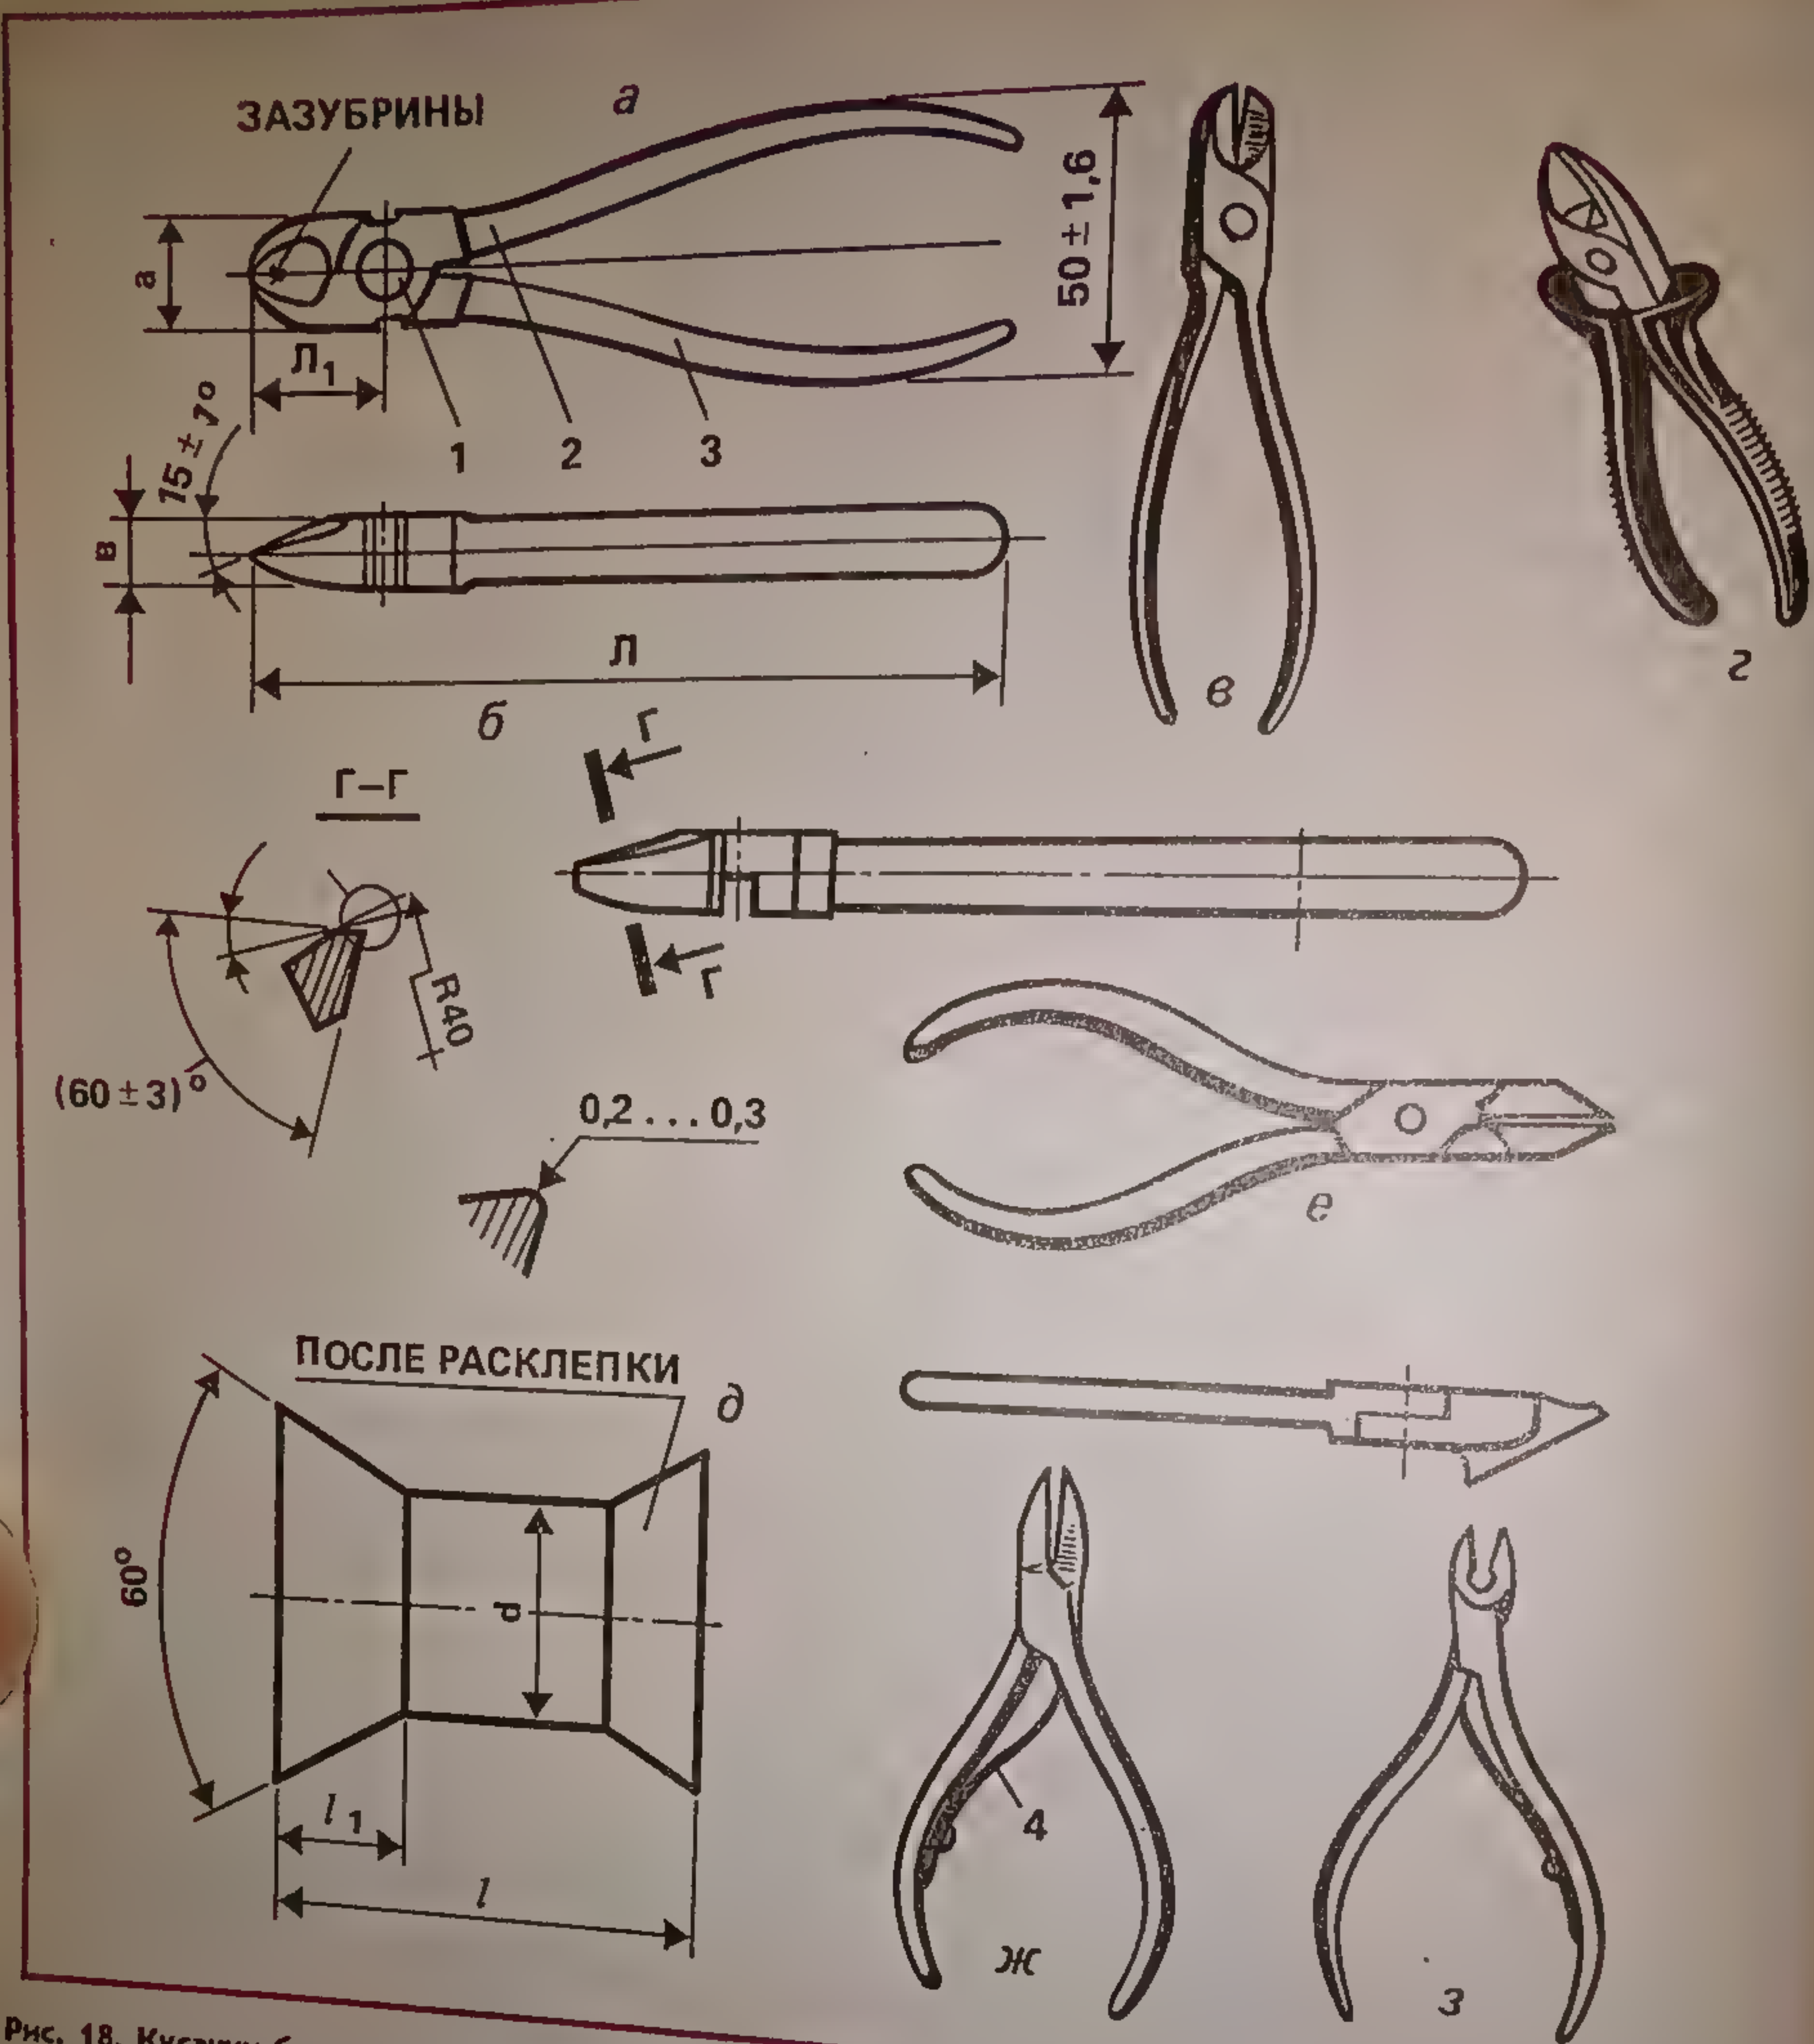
Кусачки боковые: а — без изоляции рукояток; б — сечением режущей кромки губки левого рычага; в — без изоляции рукояток; г — с изоляцией рукояток; д — ось; е — с режущими кромками под 45° ; ж — туалетные маникюрные для ногтей; з — туалетные маникюрные для заусенцев; 1 — ось; 2 — рычаг правый; 3 — рычаг левый; 4 — откидная пластинчатая пружина
